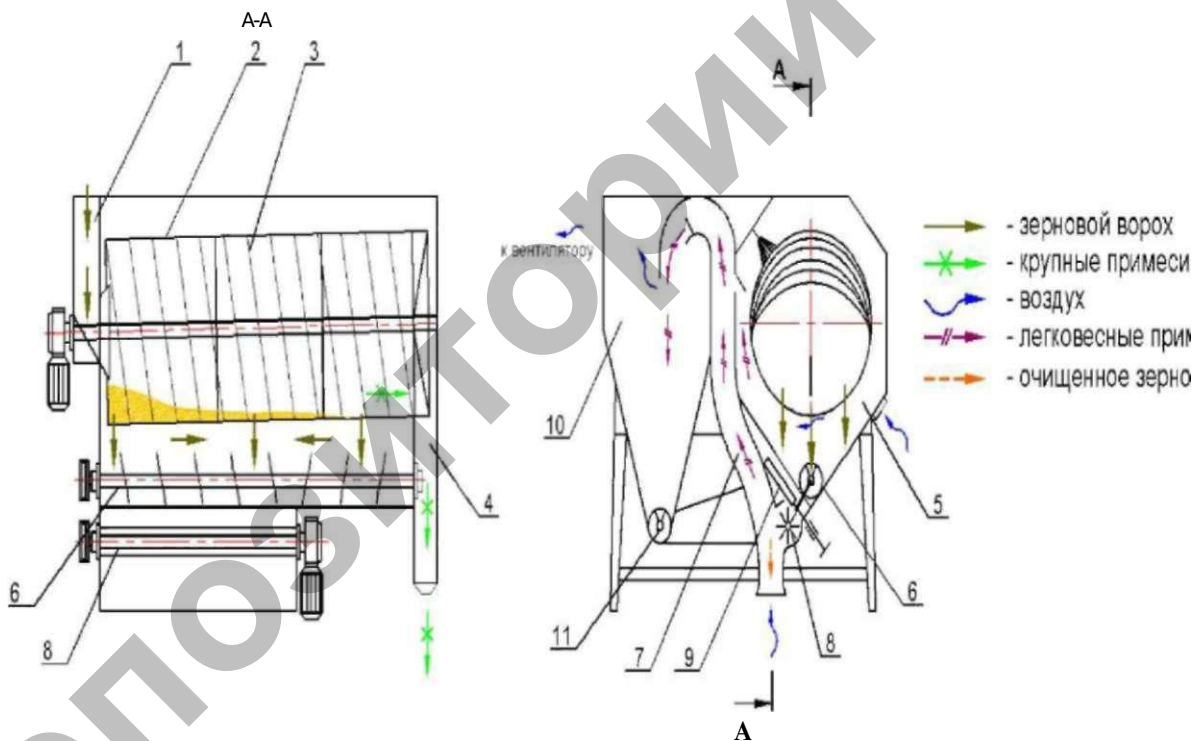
Схема работы очистителя зернового вороха ОЗЦ-50А:
